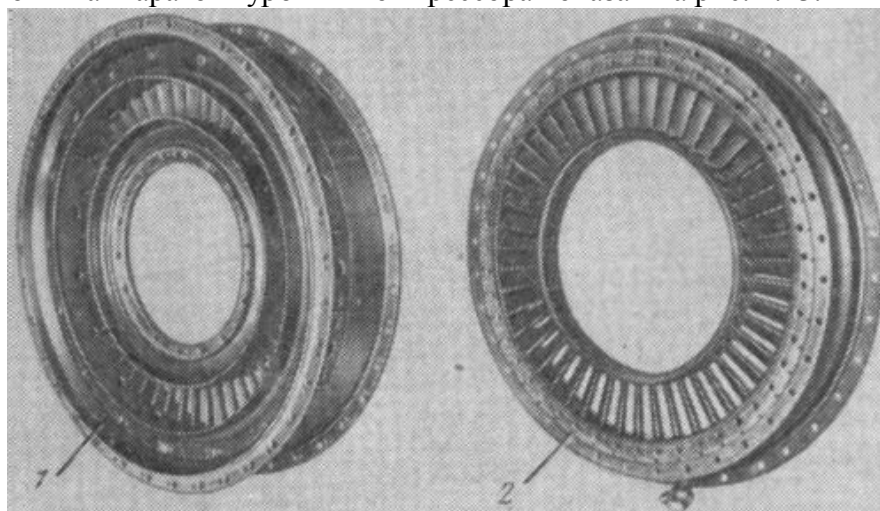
Сопловые аппараты турбины компрессора (внешний вид):
